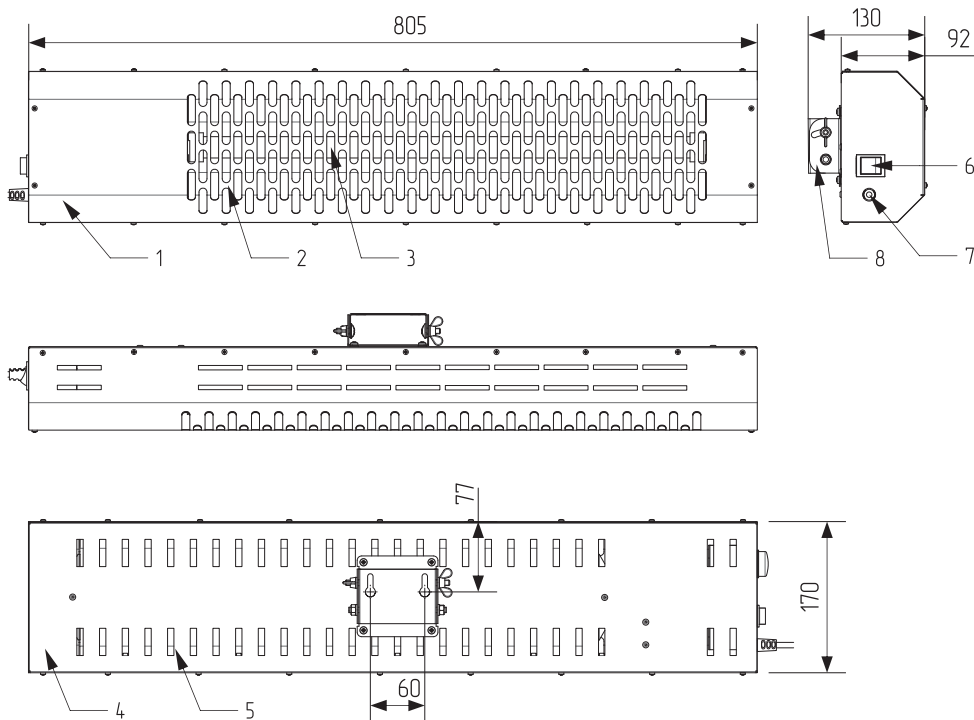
Габаритный чертёж и элементы конструкции электрического обогревателя «Пихта» СБИ-1500, СБИ-2000.
